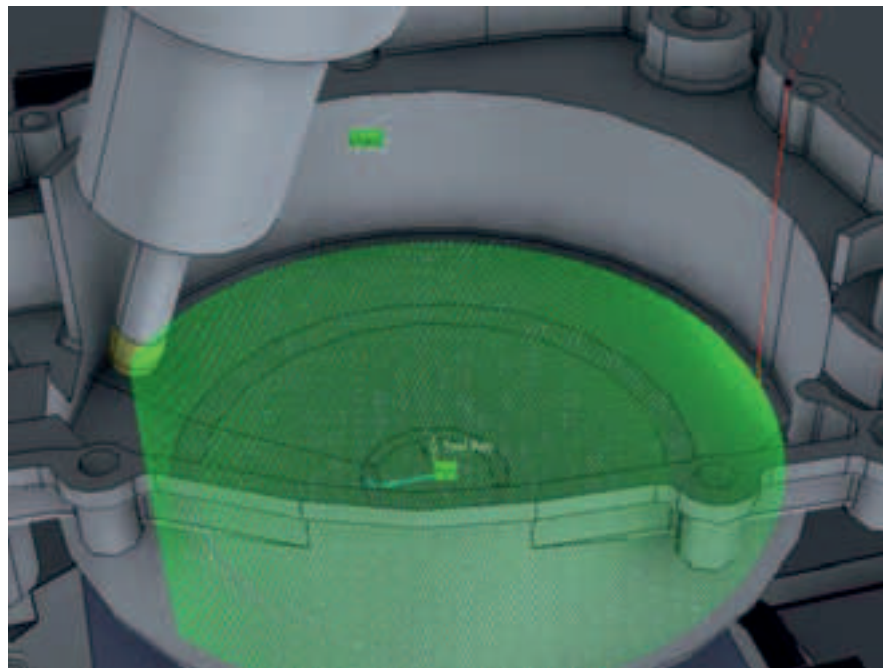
Werkzeugbahnsimulation Kopierfräsen mit angestellter Werkzeugachse
